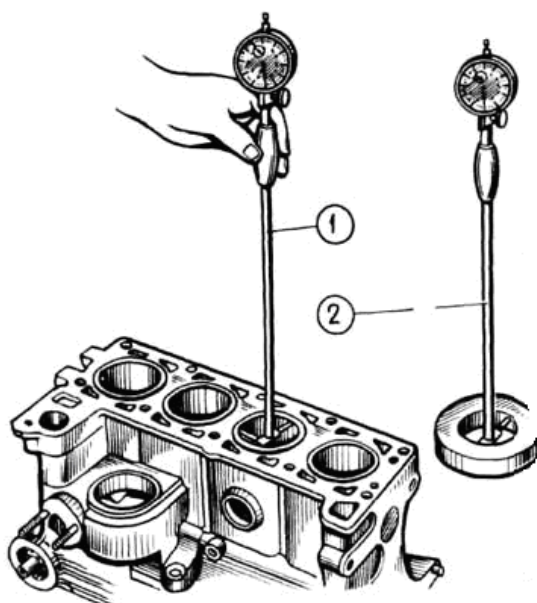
Измерение диаметра цилиндра нутромером (1) и установка нутромера «на ноль» (2) с помощью кольцевого калибра
